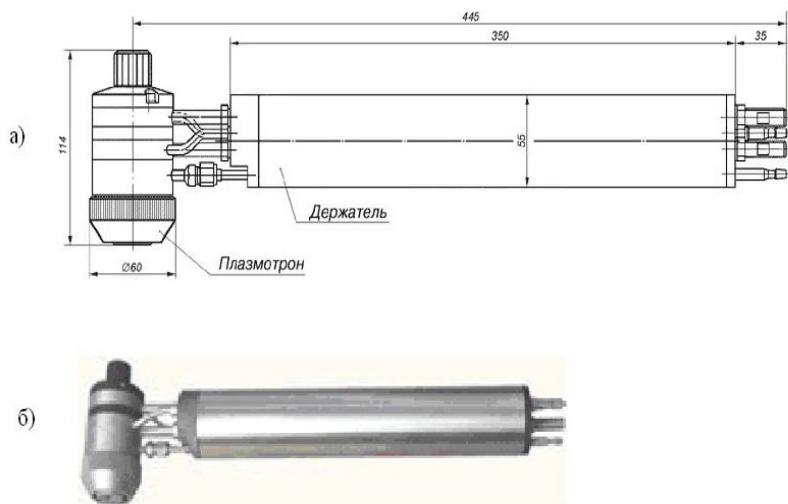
Универсальный плазмотрон для плазменно-порошковой наплавки ПП-6-03: а – схема плазмотрона; б – внешний вид
